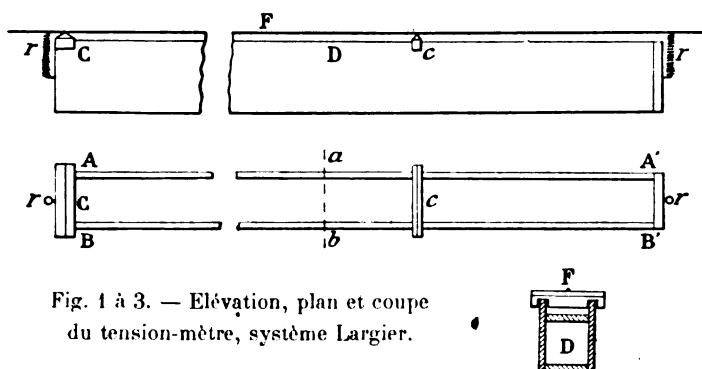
à 3. — Elévation, plan et coupe du tension-mètre, système Largier.
